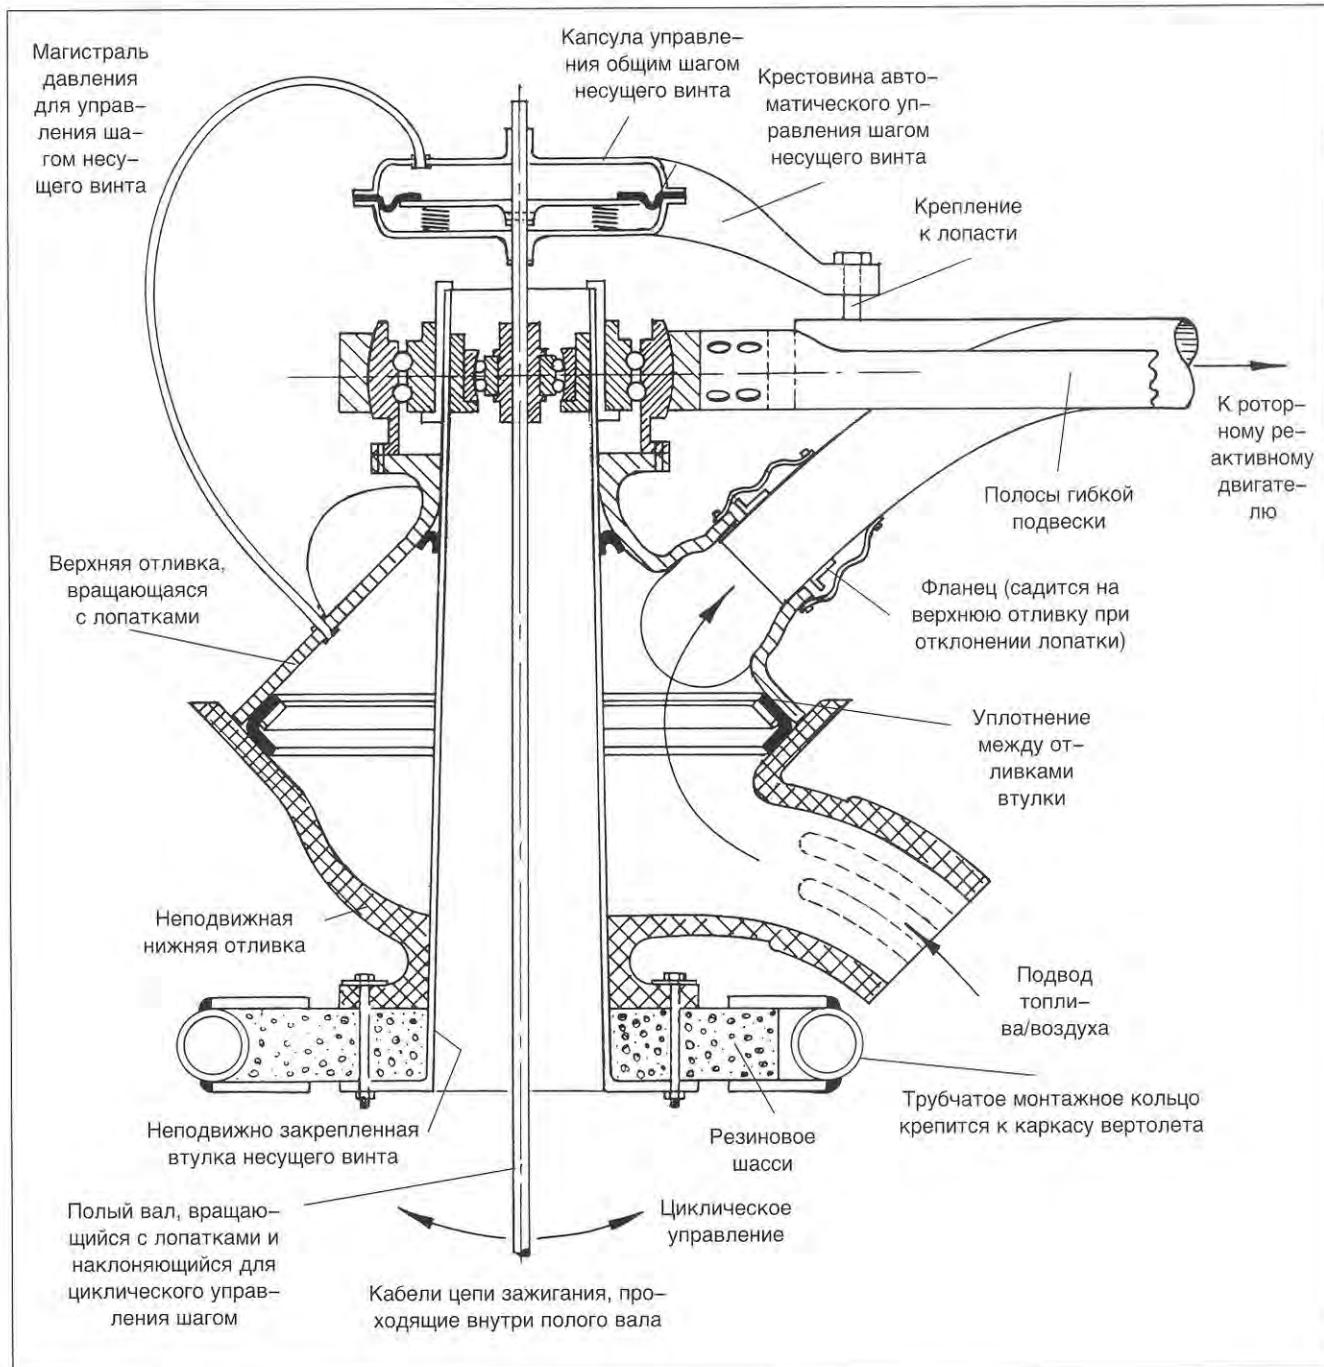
Втулка несущего винта реактивного вертолета Добльхоф WNF 342 (V4)
